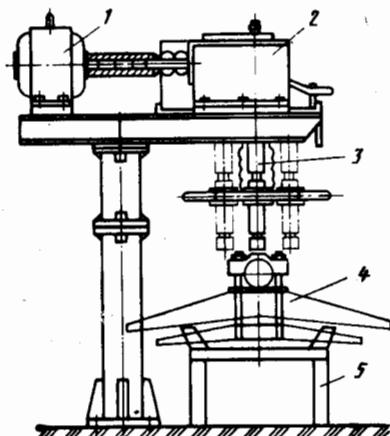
Стенд для отвертывания гаек стремянок рессор:
